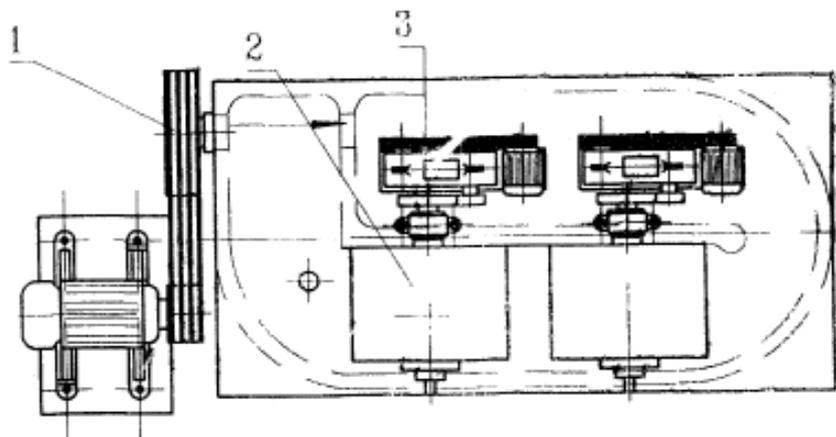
Промывная установка: 1-Привод; 2- Вакуум-фильтр барабанный; 3- Компрессор
